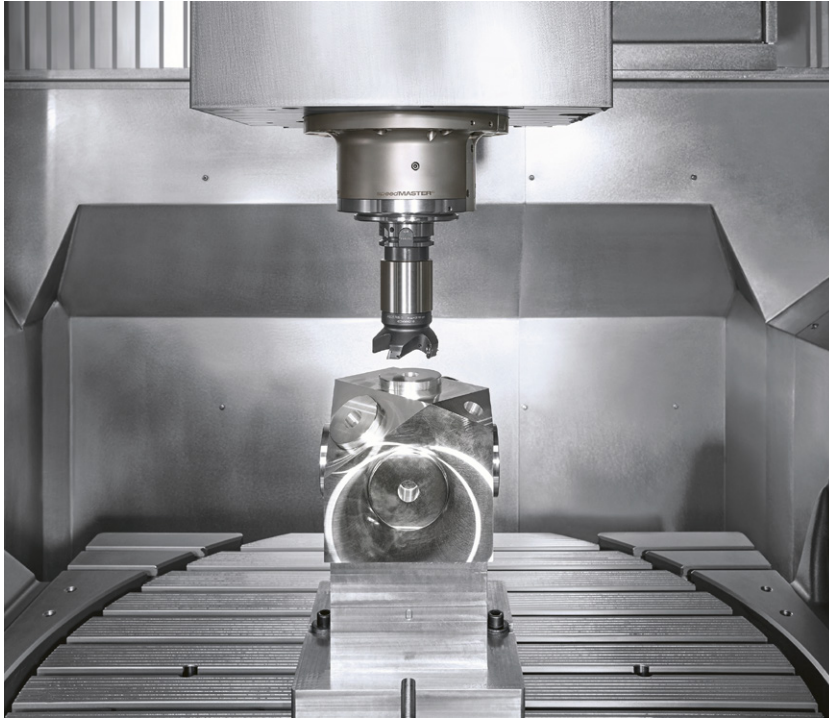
Für die Bearbeitung von Metall werden eine sehr steife Maschine und starke Motoren benötigt. Die Abbildung zeigt die Innenansicht einer DMU 95 monoblock von DMG Mori (© DMG Mori).
